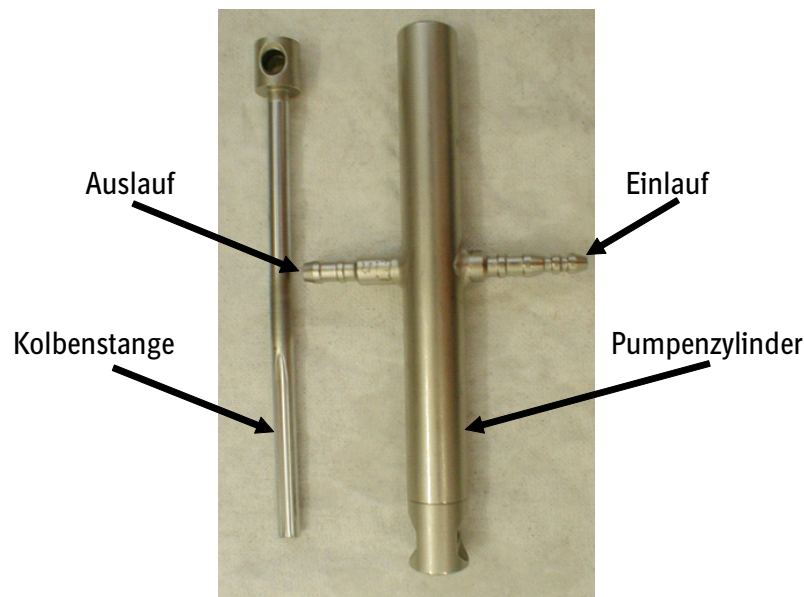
Foto Kolbenpumpe bestehend aus Pumpenzylinder und Kolbenstange
